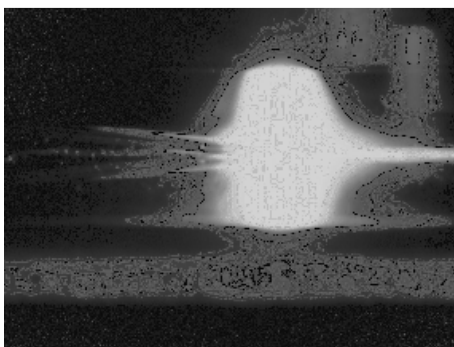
Schweißprozeß mit Kaltdrahtzufuhr
